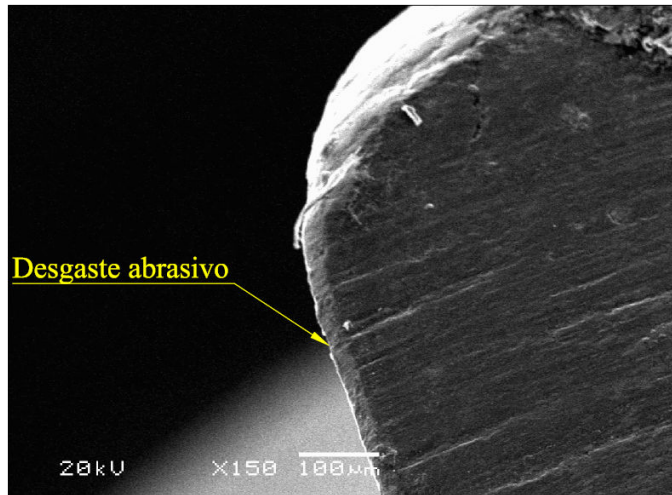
Flanco de uma das brocas com AlCrN, após teste de usinagem
